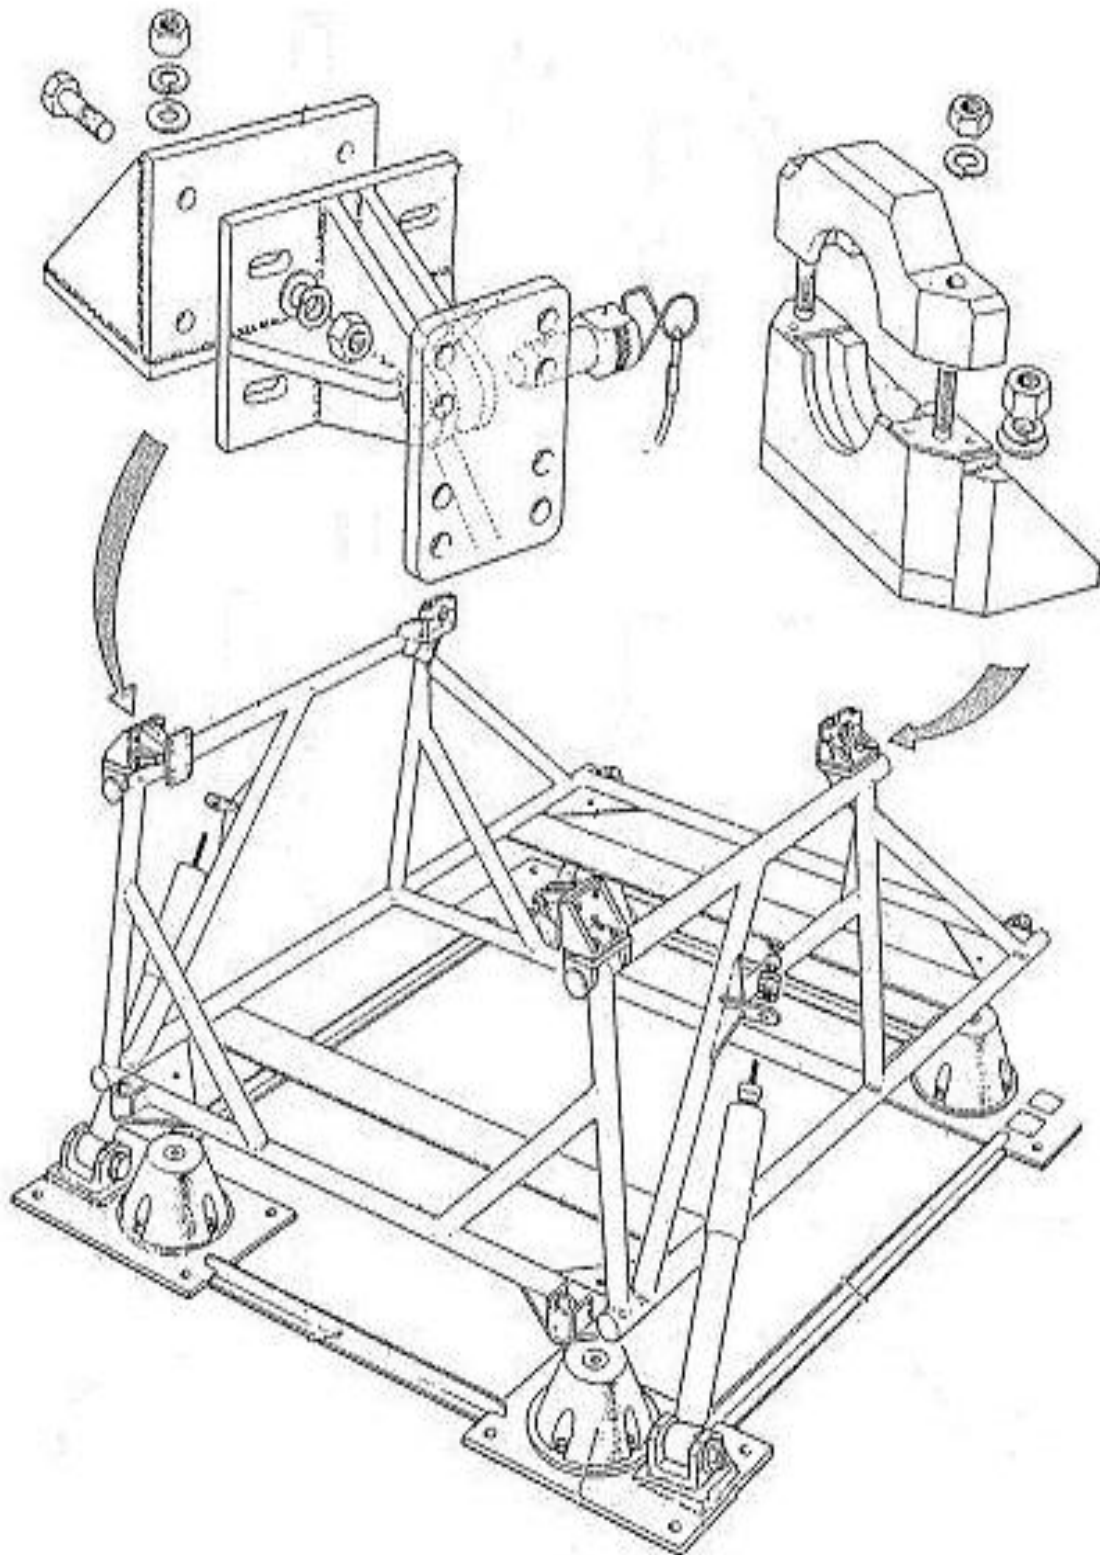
Banco Soporte Fijo del Motor Viper 535.
